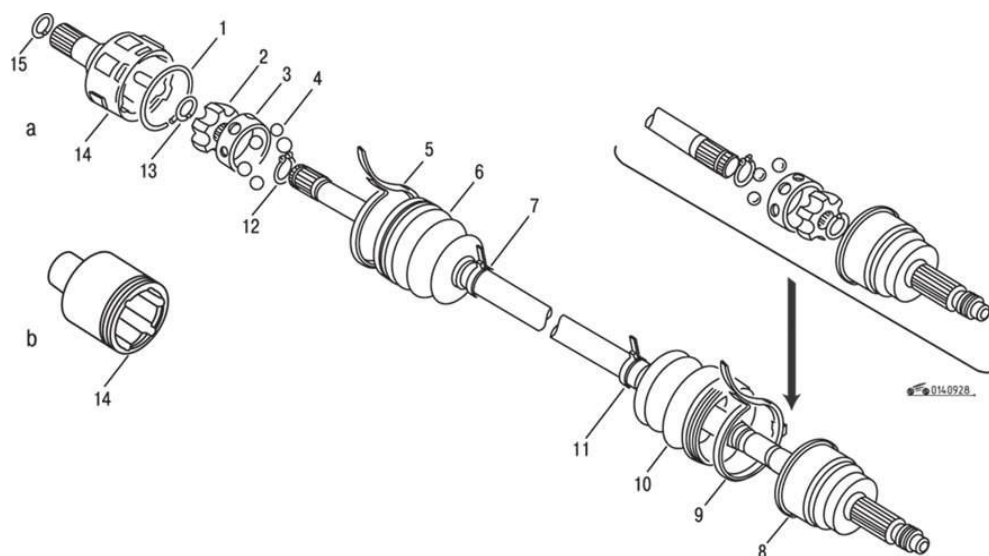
Привод переднего колеса Mazda 626 / MX-6
